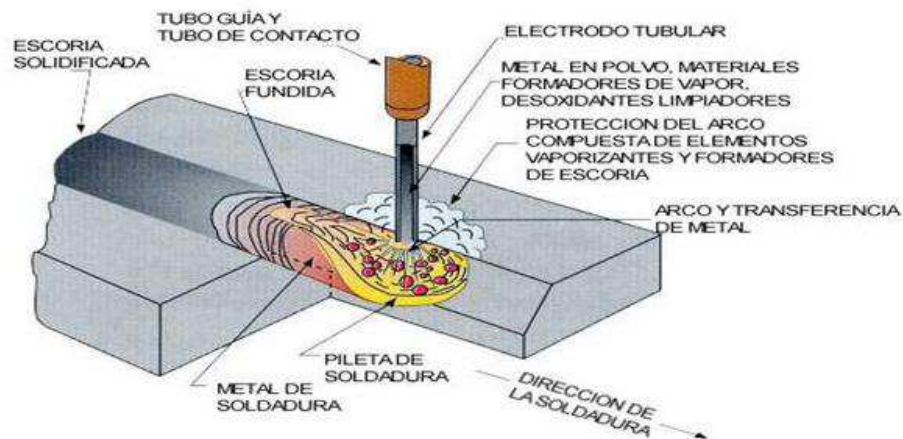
Proceso de soldadura por arco con alambre protegido por gas.
